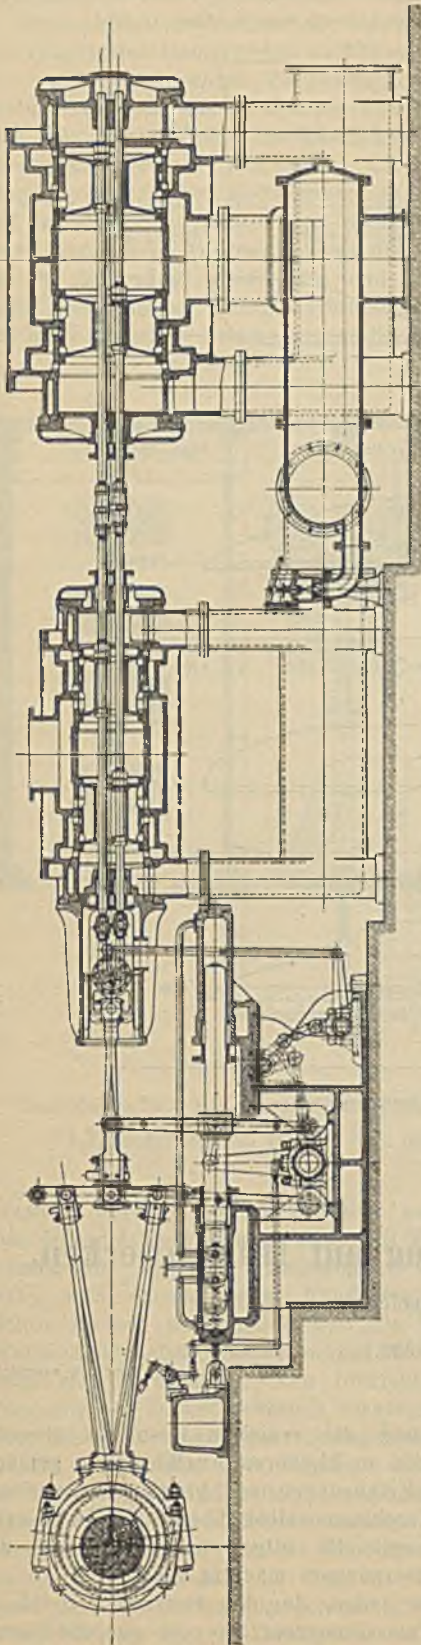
Zwillings-Tandem-Reversiermaschine.
